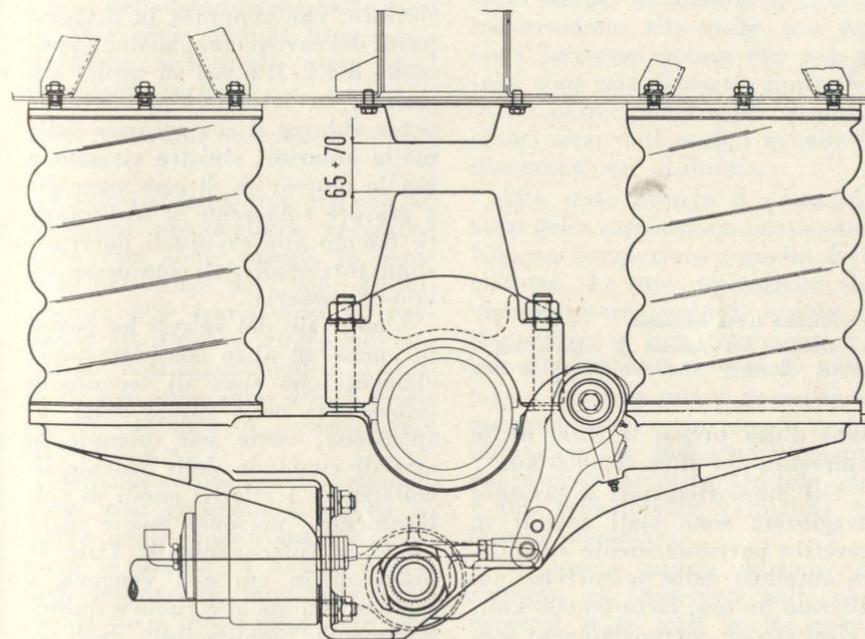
Particolare della sospensione posteriore vista da sinistra.
